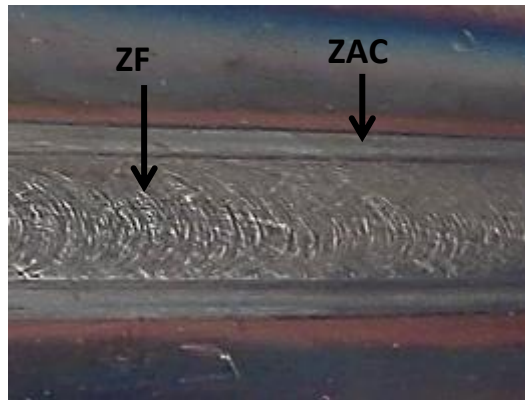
Soldadura producida por el proceso GTAW. Acero A.
